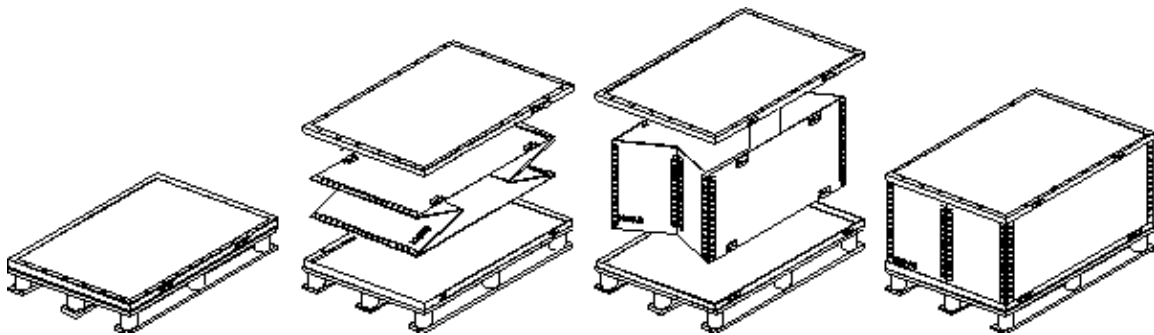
Doblado plano de contenedor de madera colapsable [7]
